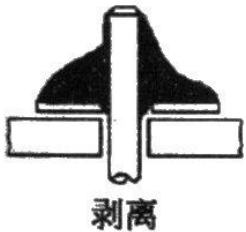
焊盘孔与引线间隙影响焊接质量
